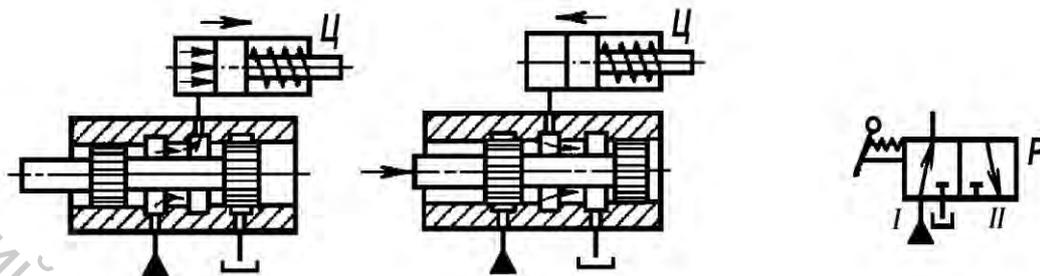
Направляющий распределитель 3/2 с цилиндрическим золотником в положениях I, II
